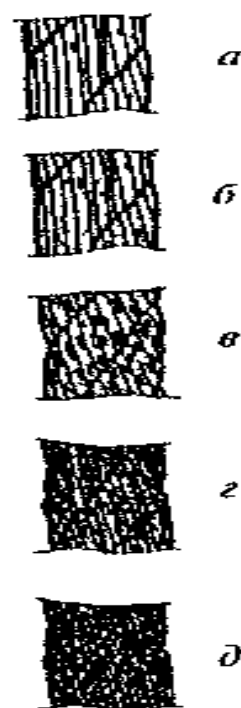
Поверхностная коррозия проволок крестовой свивки
